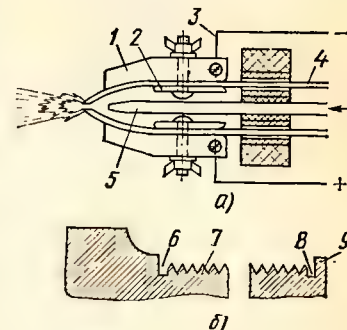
Устройство распылительной головки (а) и подготовка поверхности под напыление (б)
